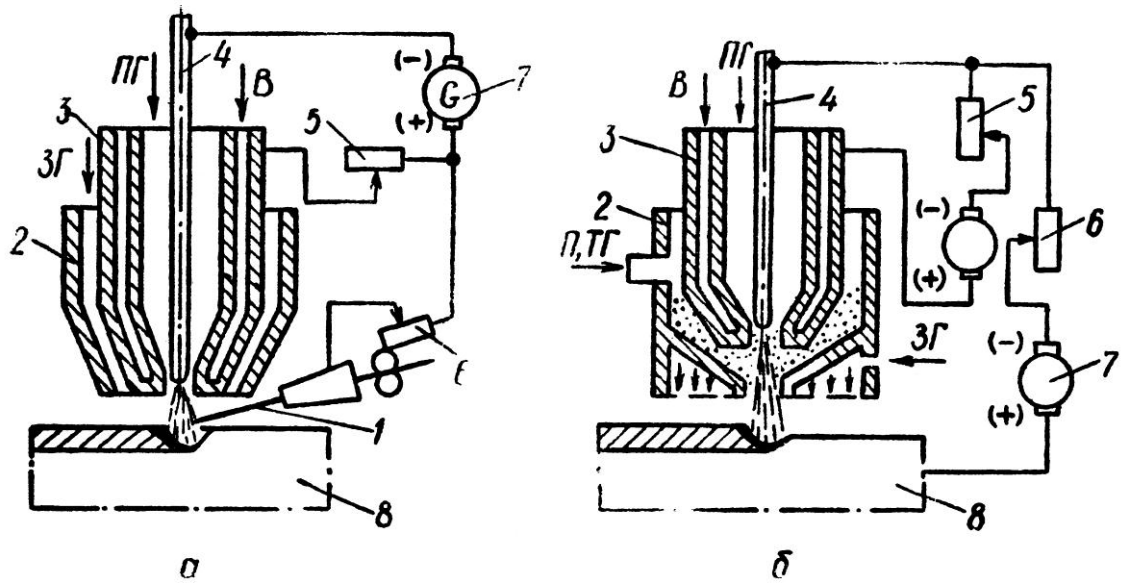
Схема плазмово-дугового наплавлення присадним дротом (а) і металічним, порошком (б):
